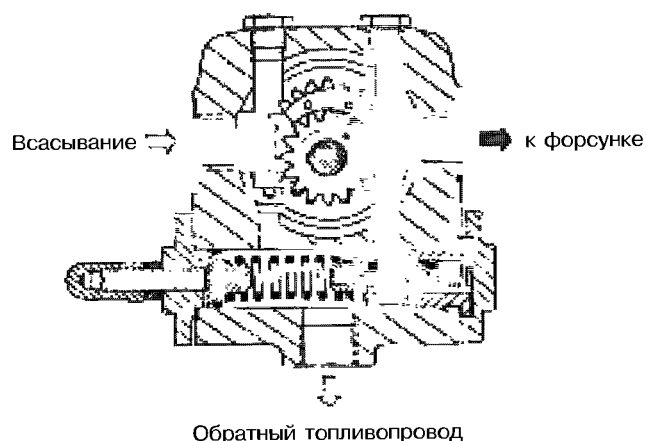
Шестерёнчатый топливный насос для моноблочной горелки на жидком топливе
